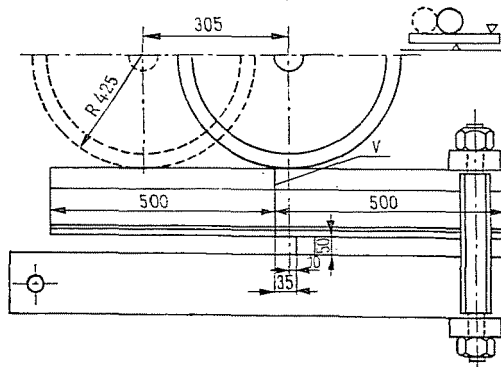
Einseitig eingespannter Schienenprüfkörper v-Schweißverbindung
